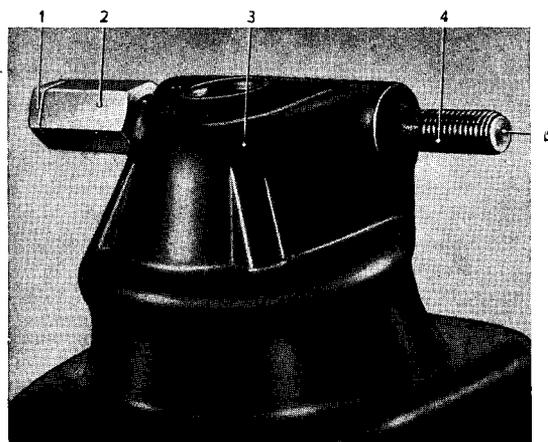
Montagehülse auf Lenkerachse geschraubt
